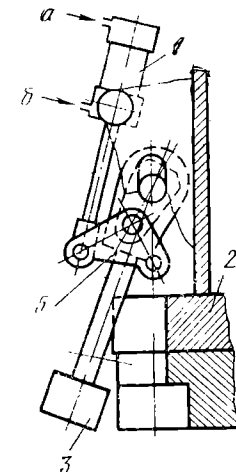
Схема зажимного устройства: 1 — гидравлический цилиндр, 2 — ползун, 3 — захват, 4 — штамп, 5 — рычаг, 6 — шток цилиндра; а — давление масла на разжим, б — давление масла на зажим
